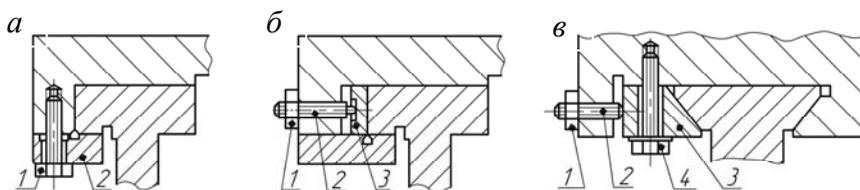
Способы регулирования зазоров в направляющих скольжения прижимной планкой (*а*), регулировочной незакрепляемой (*б*) и закрепляемой (*в*) после регулирования планками
